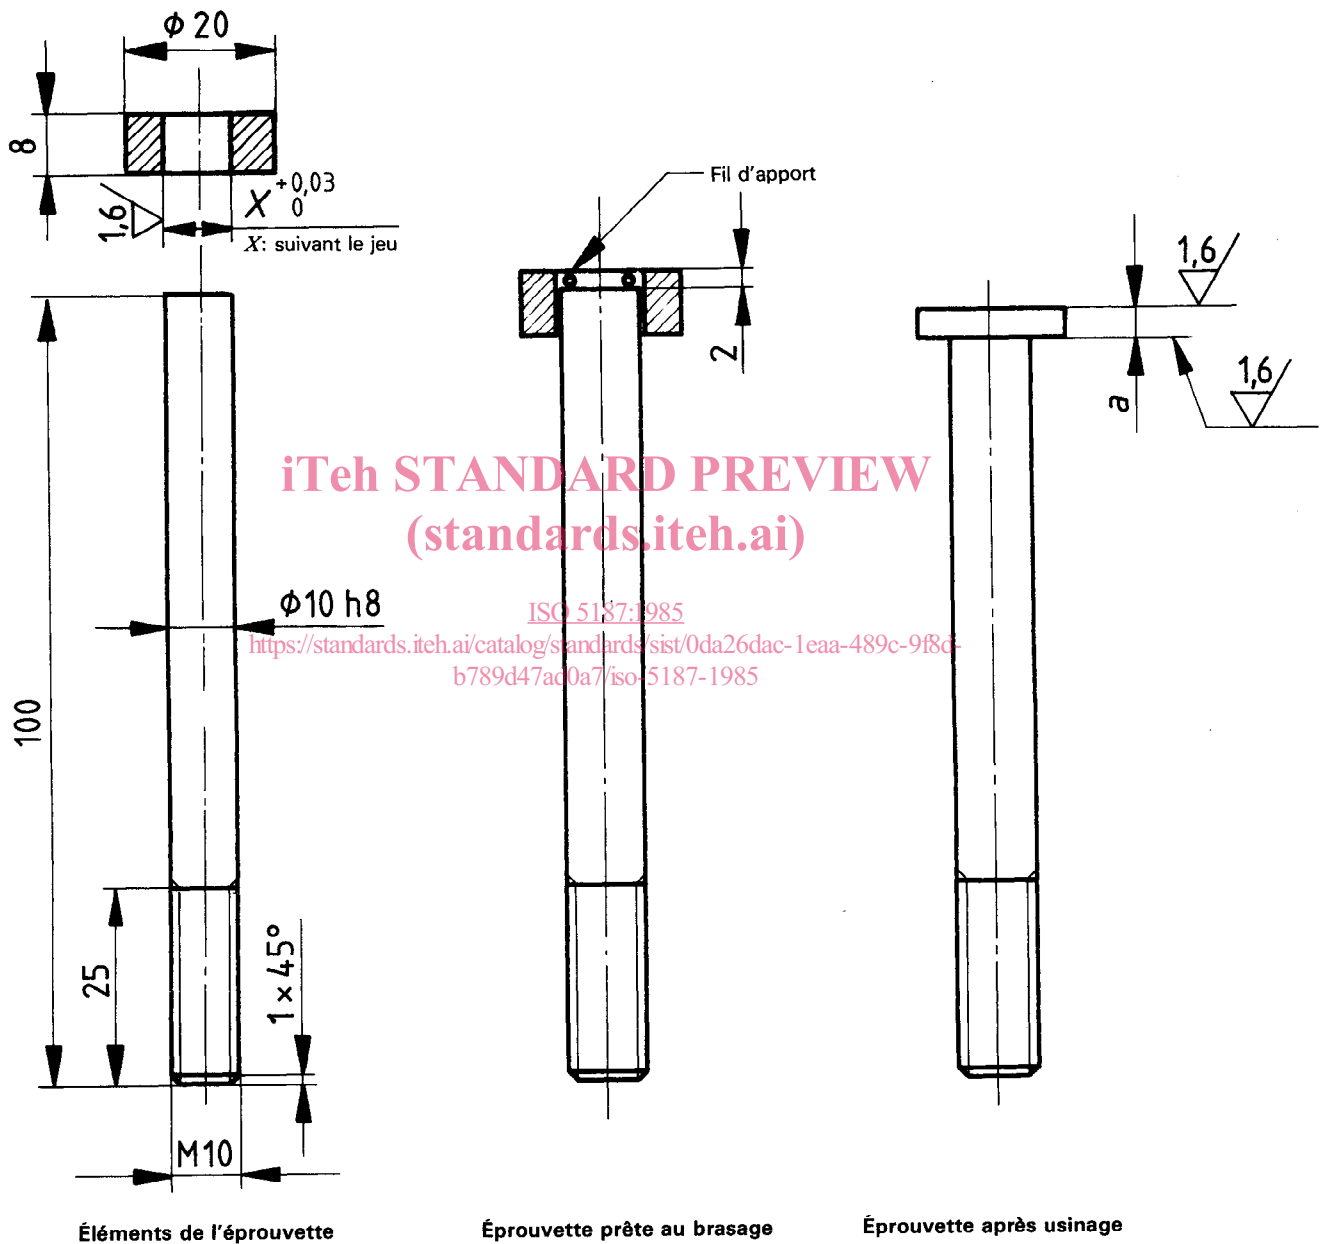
Dimensions de l'éprouvette de cisaillement type I
